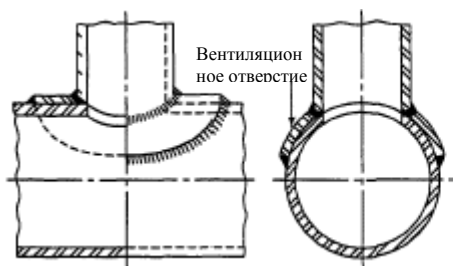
(В). Типичное сварное патрубковое присоединение с дополнительным усилением.
